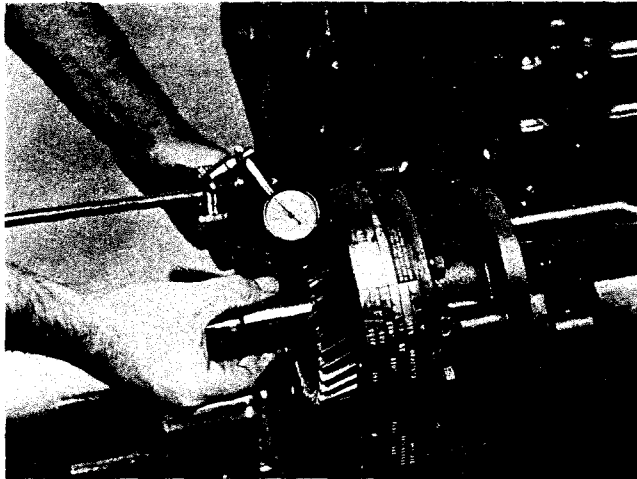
, (N114263). Revisión del juego en el engranaje impulsor de accesorios.
